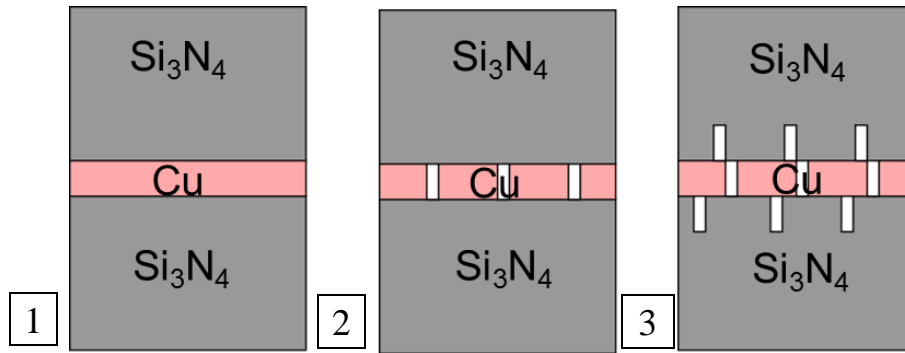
Схемы диффузионно-сварных соединений типа керамика-медная прокладка-керамика: 1 – со сплошными медными прокладками; 2 – с перфорированными медными прокладками; 3 – с перфорированными медными прокладками и с углублениями на поверхности керамики.
